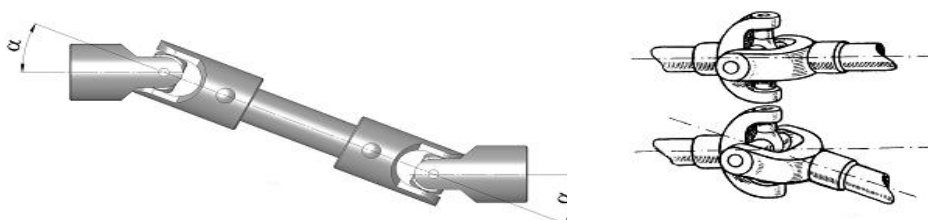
Transmisia cardanică: a) arbori cardanici, b) cuplaje cardanice.
